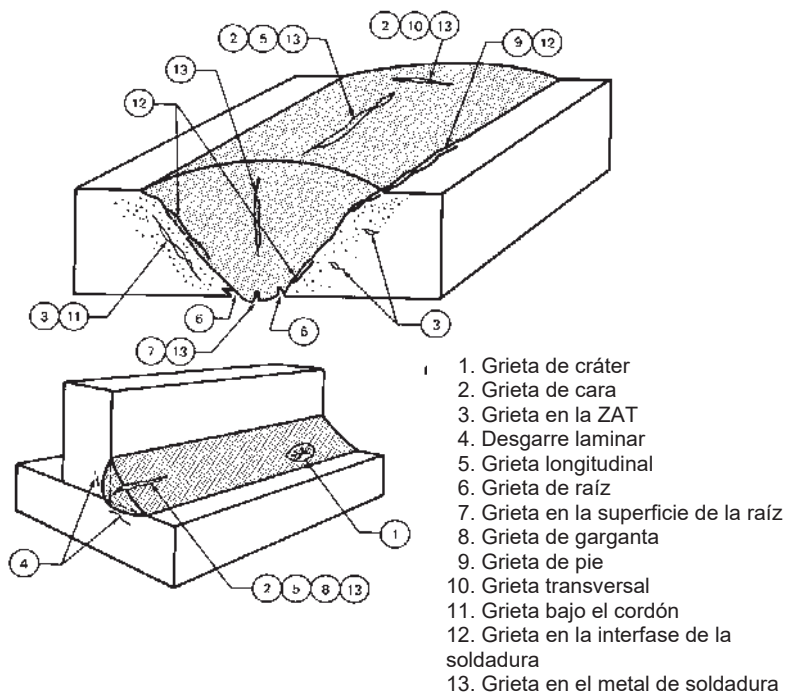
Tipos de grietas en soldadura ⁽¹¹⁾
